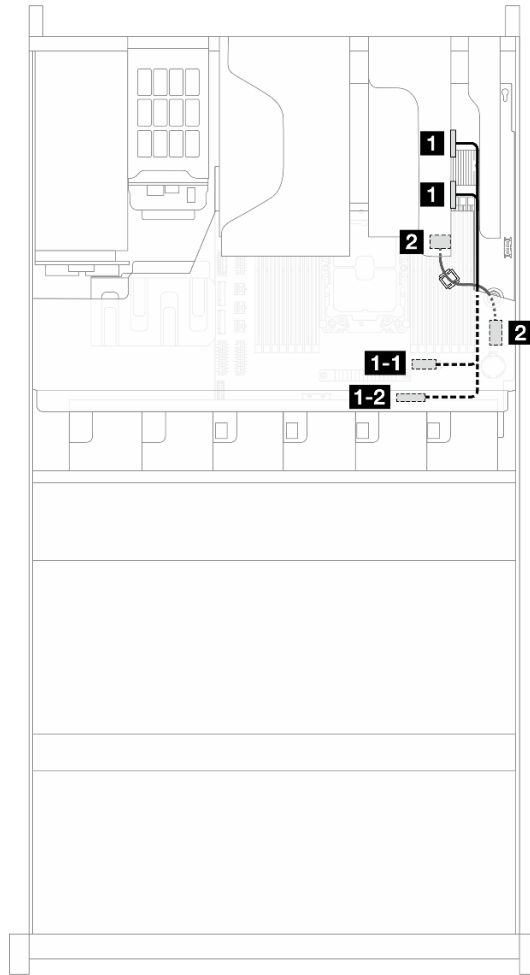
Disposición de los cables para la tarjeta de expansión 2
